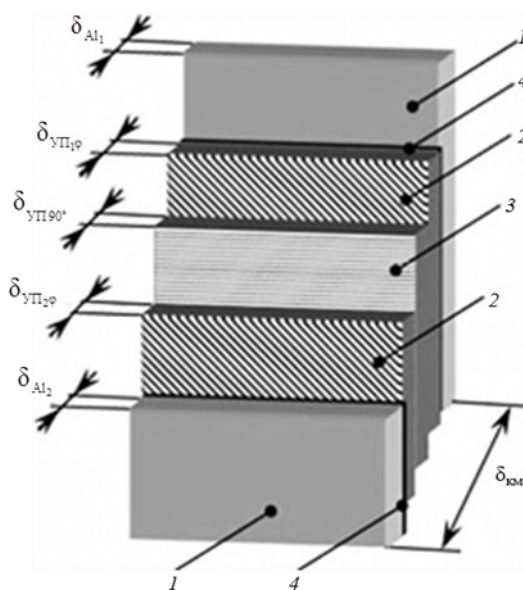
Схема пятислойного металлополимерного композита «алюминий–углепластик»:
